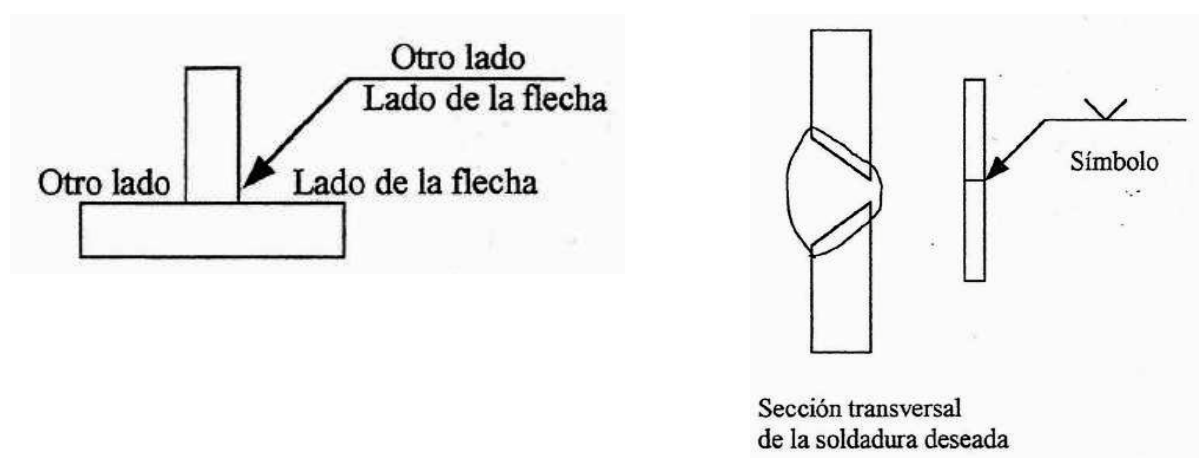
SÍMBOLO PARA UNA SOLDADURA DE RANURA EN "V" DEL OTRO LADO DE LA FLECHA
